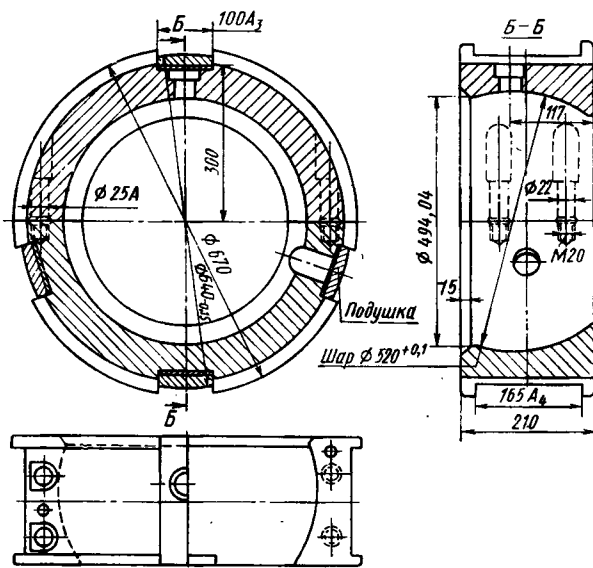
Шаровая обойма вкладыша опорно-упорного подшипника
